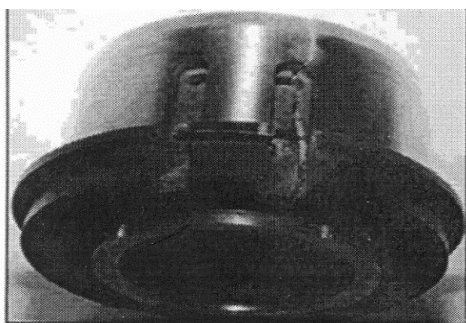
Фрезерованные пазы для гидростатического подвода конденсата
